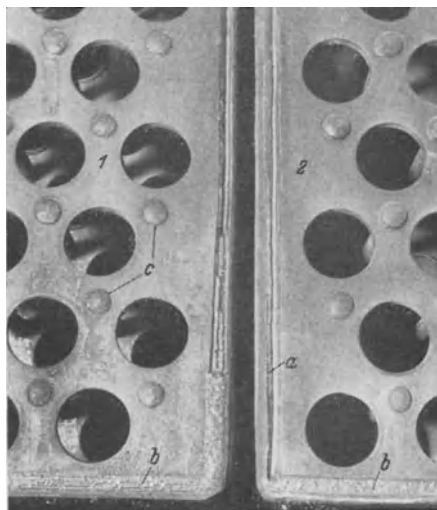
Geschweißte Umlaufbleche an einem Wasserkammerkessel.
